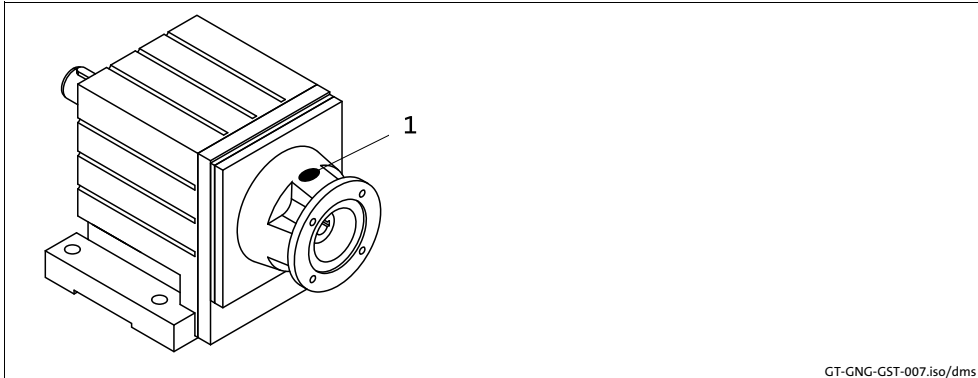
GNA-Normmotor mit Flansch, Lage der Verschlusschraube (1)
